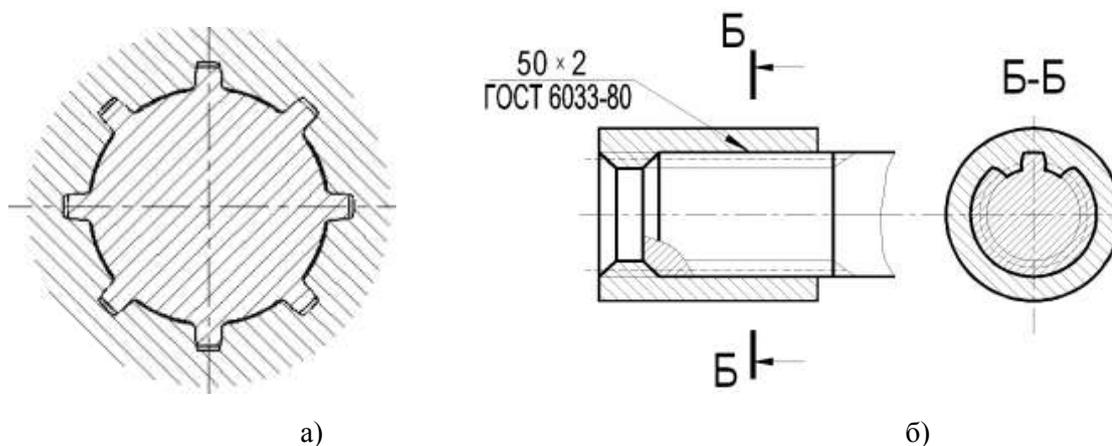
Шлицевое соединение: а) эвольвентный профиль; б) изображение и обозначение эвольвентного зубчатого соединения
